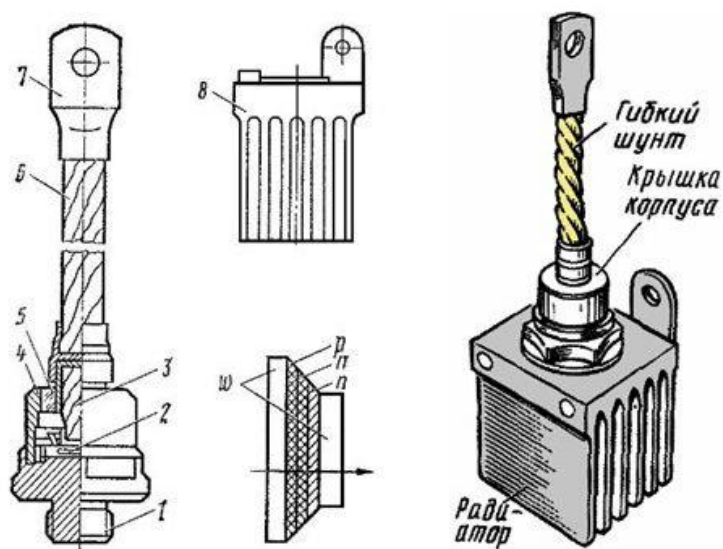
Вентиль ВЛ200-8 выпрямительной установки ВУК-4000.
